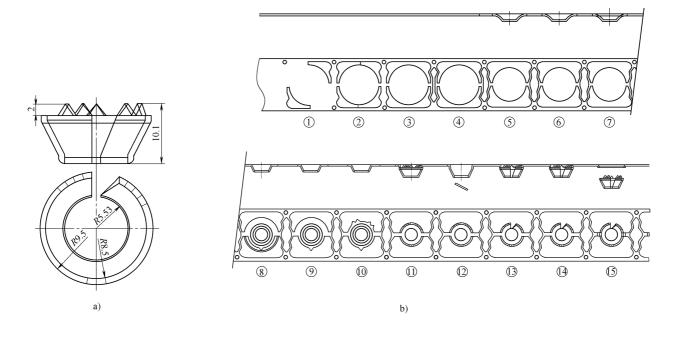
锥形件级进模 a) 零件图 b) 排样图
